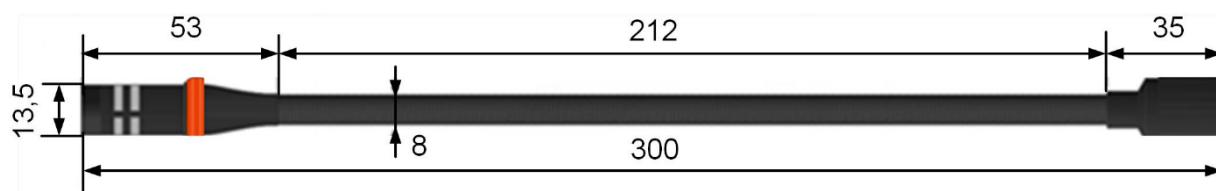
Внешний вид и габаритные размеры микрофона типа «гусиная шея»
